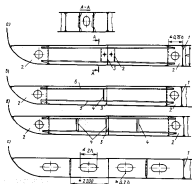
Открытие флюгов: а — бракетный; б — бракетный со стойкой у стрингера; в — бракетный с промежуточными вторыми стойками; с — облучечный
